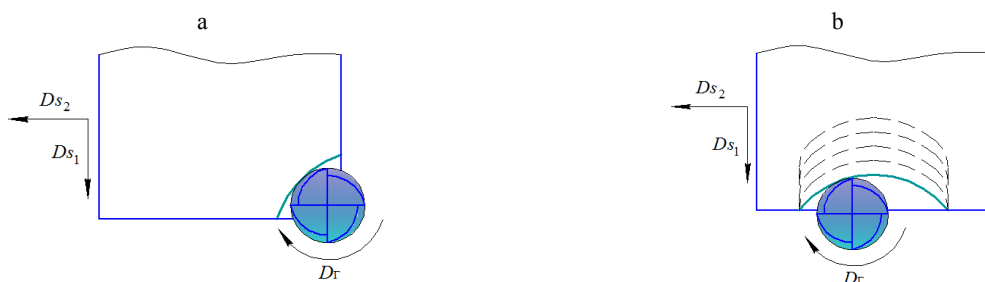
Схемы обработки с врезанием фрезы по дуге: а – уступа; б – полузакрытой полости
